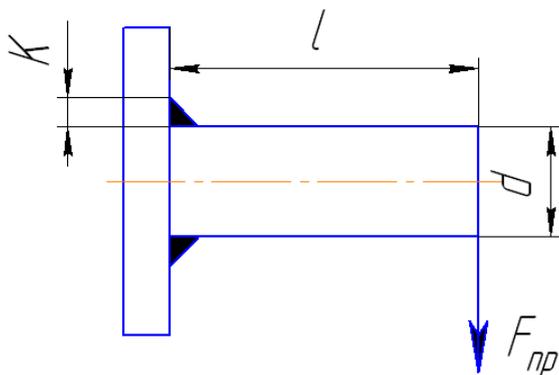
Схема расчета сварочного шва пальца пружины.
